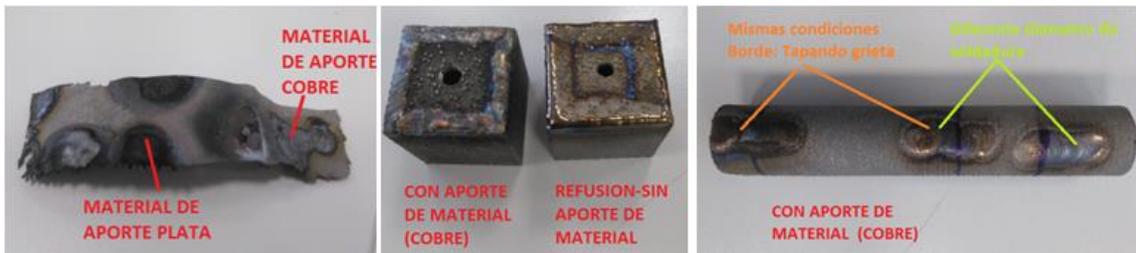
Preparación de borde de piezas de FA que van a ser soldadas
